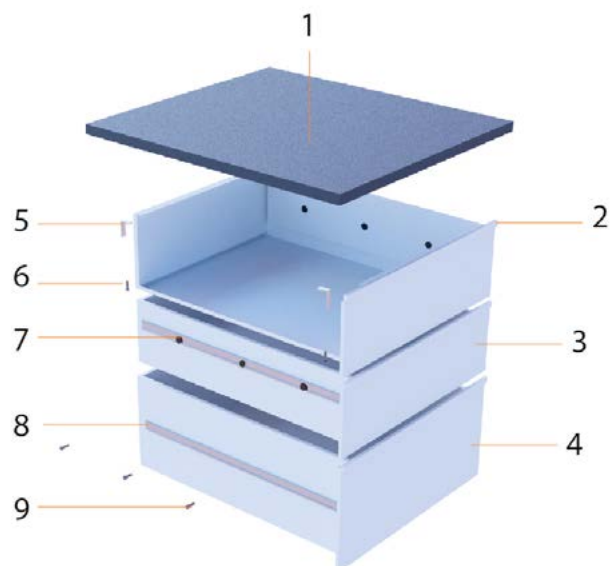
Detalle constructivo 3d cajonera con mesón de acero inoxidable
